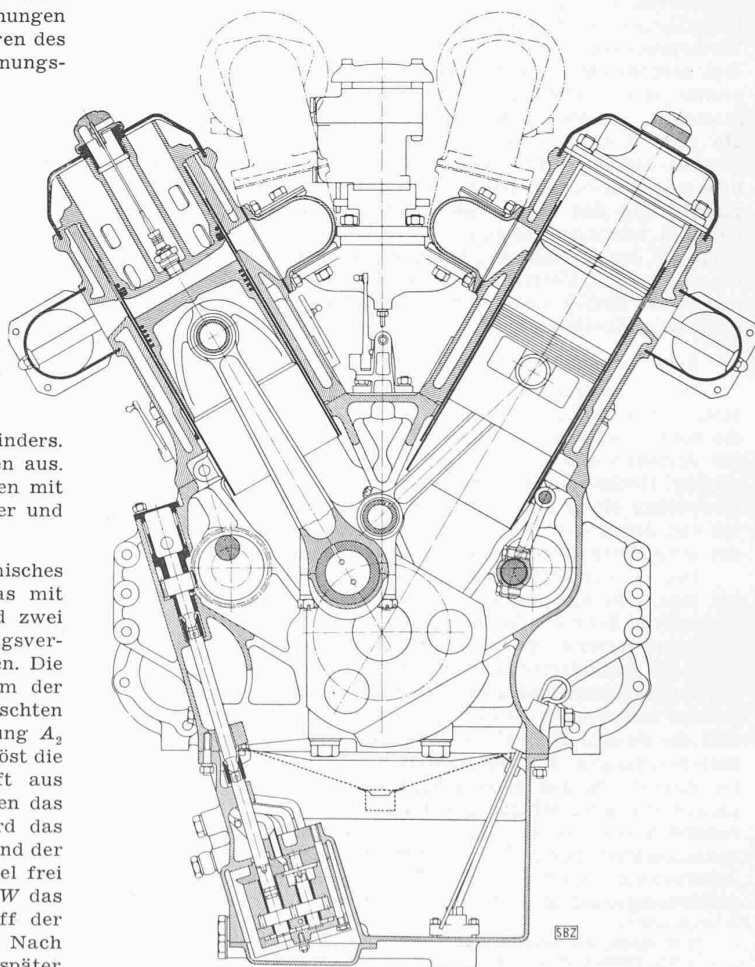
Ventilloser Zwölf-Zylinder Holzkohlengas-Motor Bauart Panhard-Levassor für 270 PS. — Schnitt 1:8
